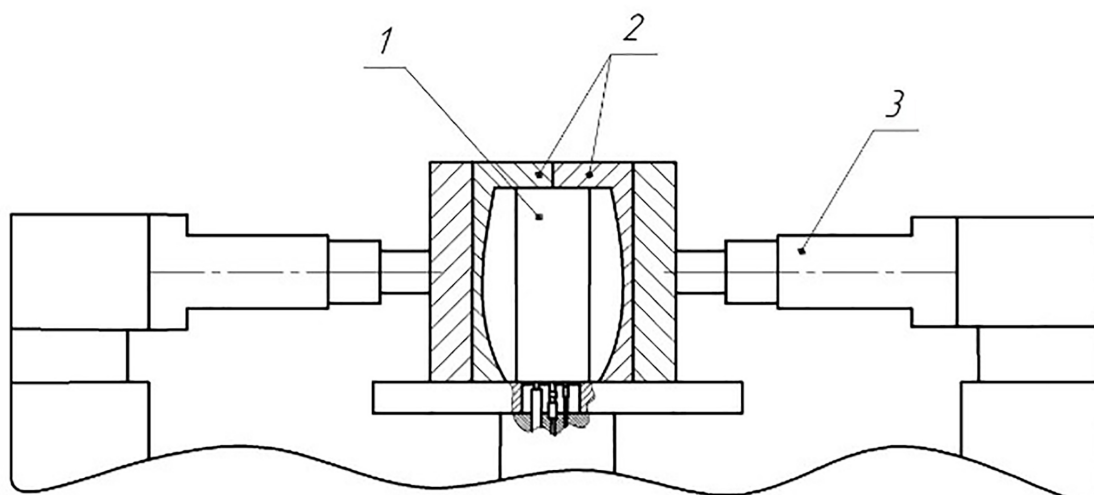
Установка для высокоскоростной штамповки взрывом
